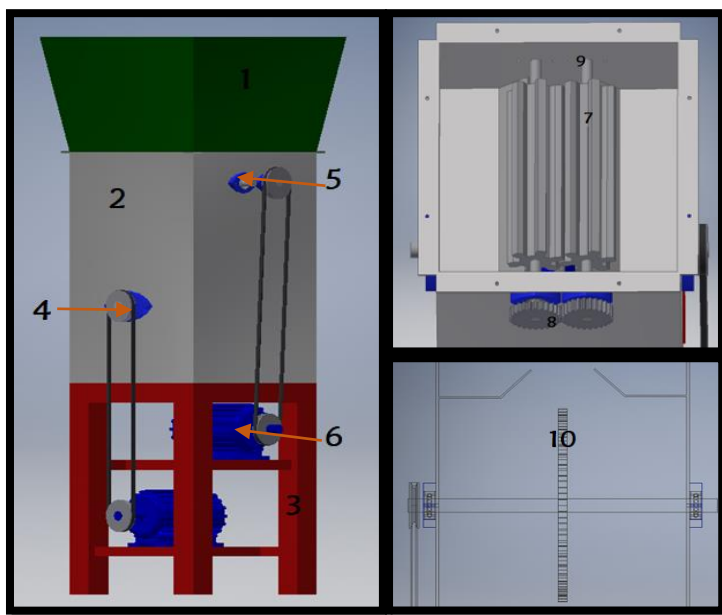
Diseño propuesto de maquina de molienda de Lirio acuático. 1. Tolva, 2. Caja, 3. Base de PTR, 4. Poleas, 5. Chumacera, 6. Motor, 7. Rodillo, 8. Engranajes, 9. Ejes, 10. Sierra.
